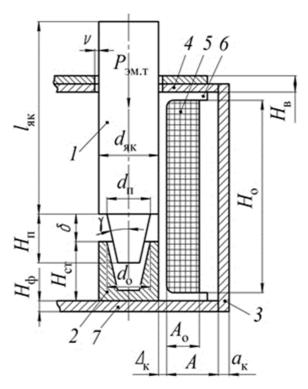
эскиз втяжного электромагнита реле РВ100: 1 – якорь; 2 – стоп; 3 – корпус; 4 – воротничок; 5 – обмотка; 6 – каркас; 7 – опорный фланец
